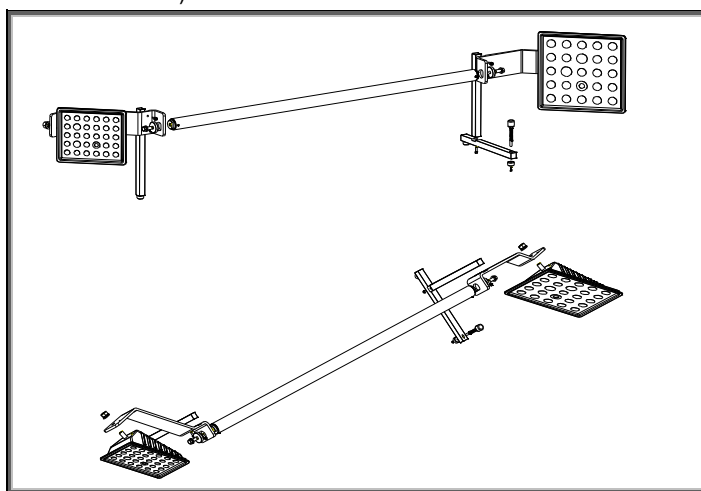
Развернутый рисунок порядка сборки калибровочной системы
